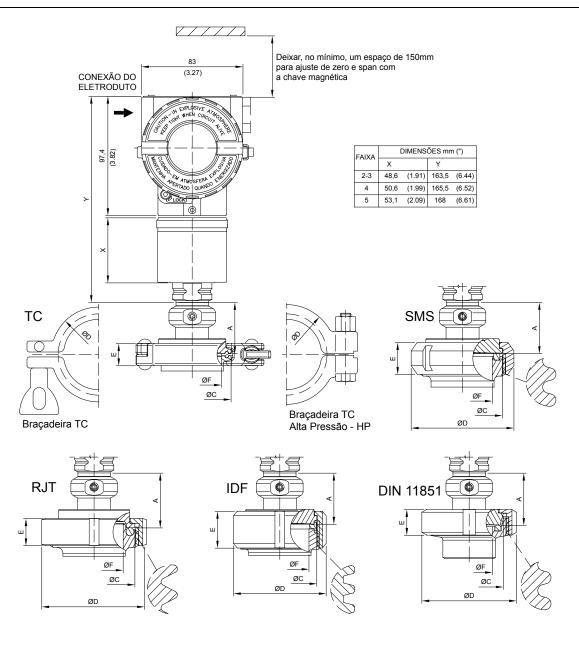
(a) - Desenho Dimensional de Montagem do LD290
